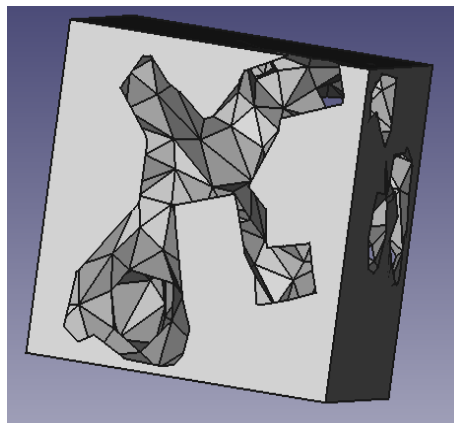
Diseño de molde para impresión inversa 3D del andamio
